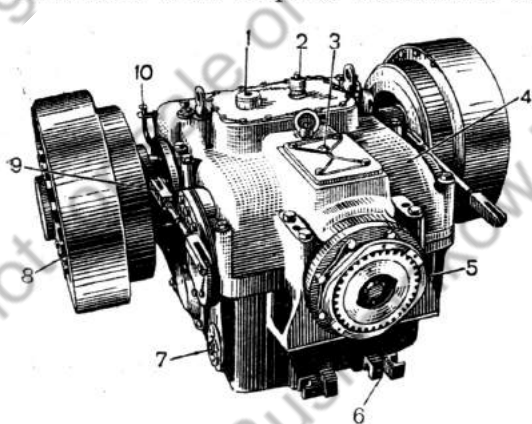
Коробка перемены передач вместе с планетарными механизмами поворота (внешний вид): 1 — пробка для заливки масла; 2 — сапун; 3 — пробка для замера уровня масла; 4 — верхняя половина картера; 5 — нижняя половина картера; 6 — поводковые валы; 7 — ось вилки переключения; 8 — планетарные механизмы поворота; 9 — тига; 10 — трубка с пробкой
